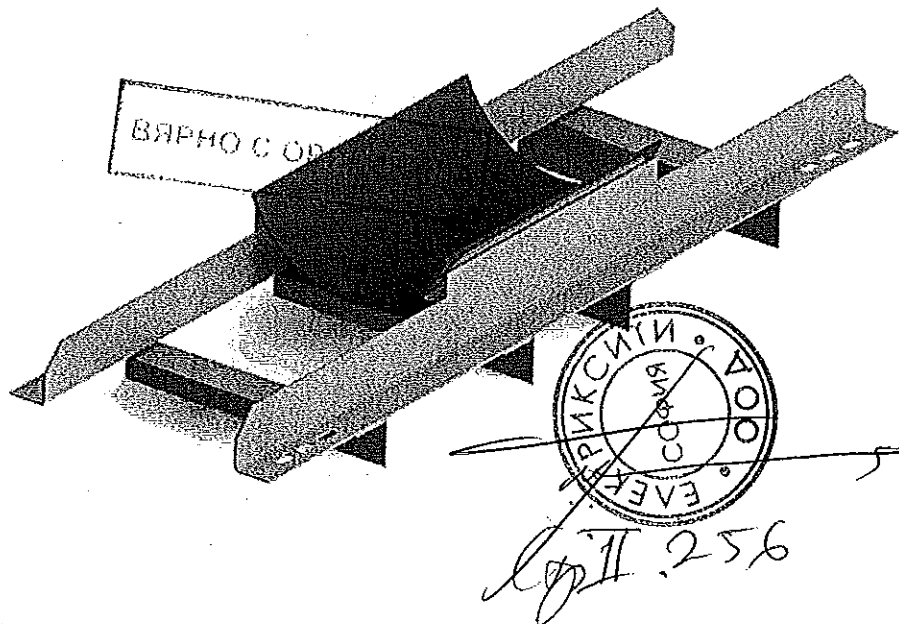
Ложементы производства ООО «РКС-пласт» для крепления соединительных муфт на металлоконструкции
